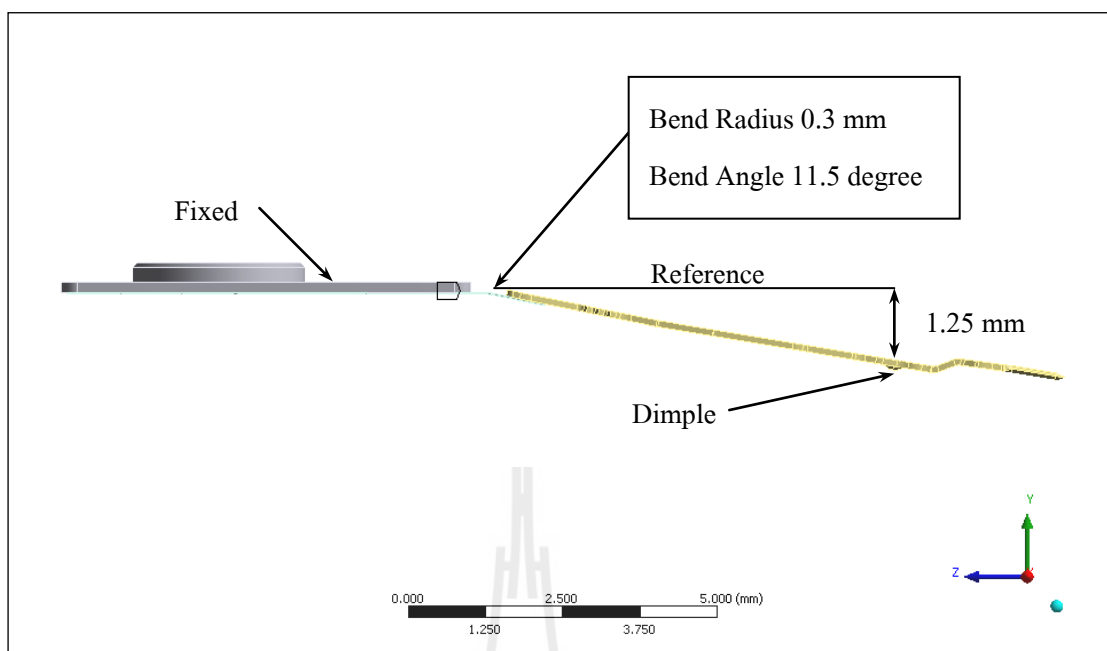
Drawing แบบจำลองของ Hinge
